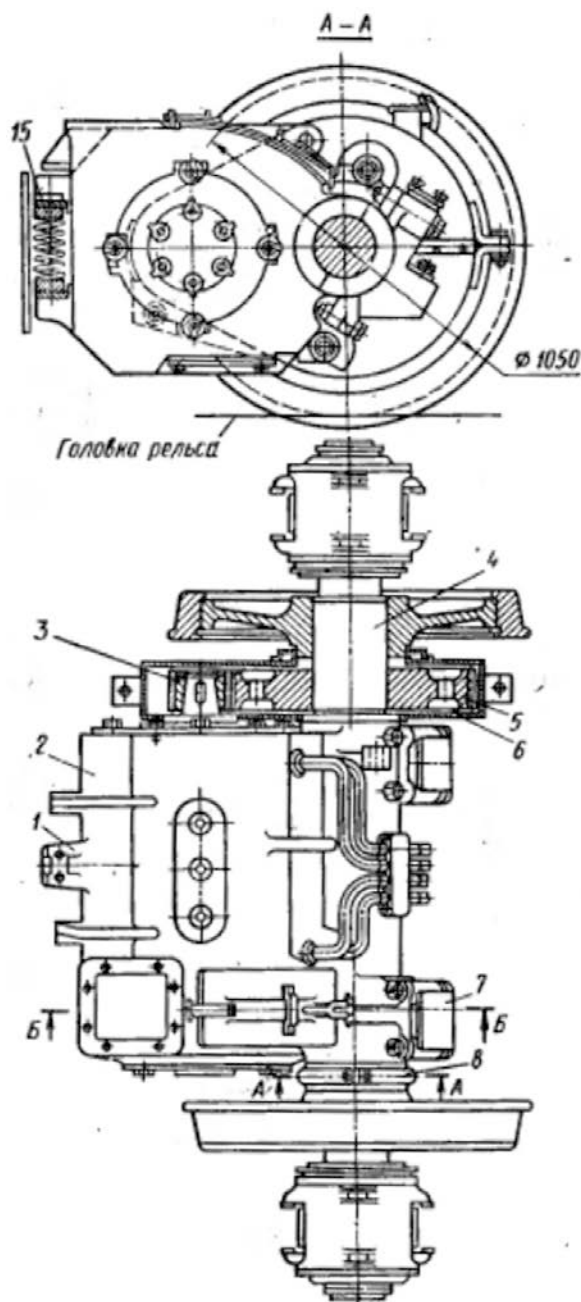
Схема опорно-осевого подвешивания электродвигателя
